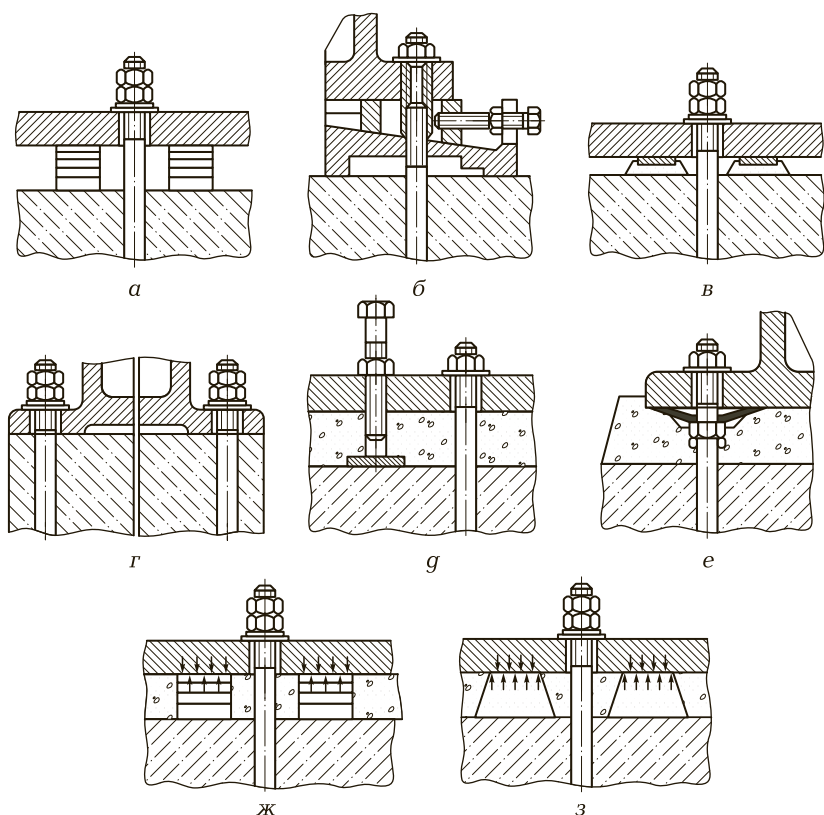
Основные конструкции стыка корпусная деталь—фундамент: а — с местной опорой на пакет прокладок; б — на опорные башмаки; в — на бетонные опоры; г — непосредственно на фундамент; д — со сплошной опорой на бетонную подливку с временной установкой при выверке на отжимных винтах; е — на установочных гайках; ж, з — со смешанной опорой на подливку и опорные элементы
